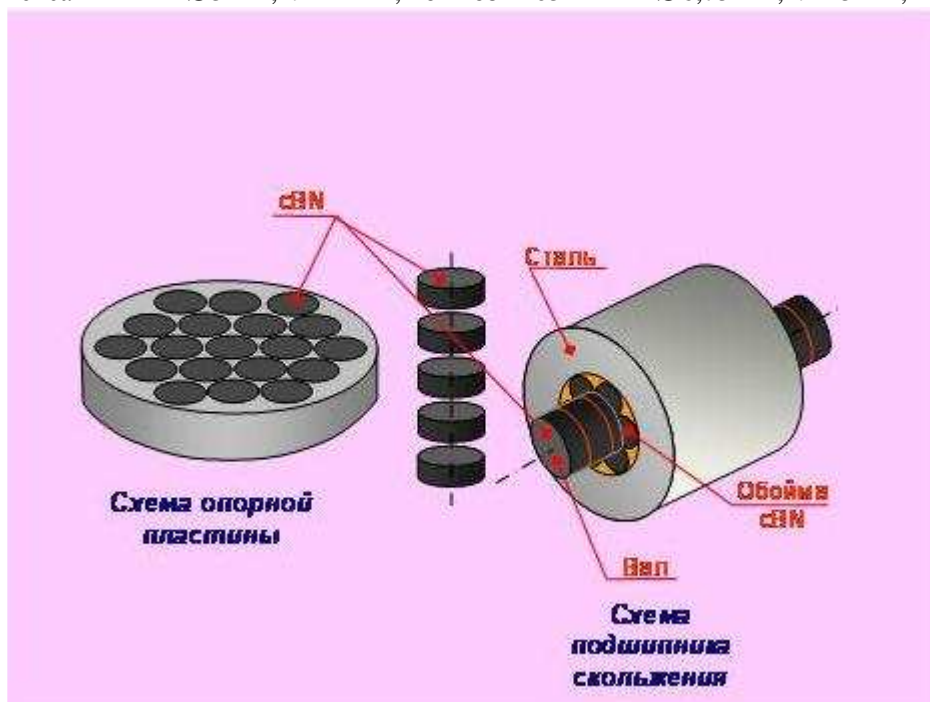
Схемы изделий конструкционного назначения из cBN: опорные пластины, оси, обоймы подшипников скольжения, полученные пайкой
